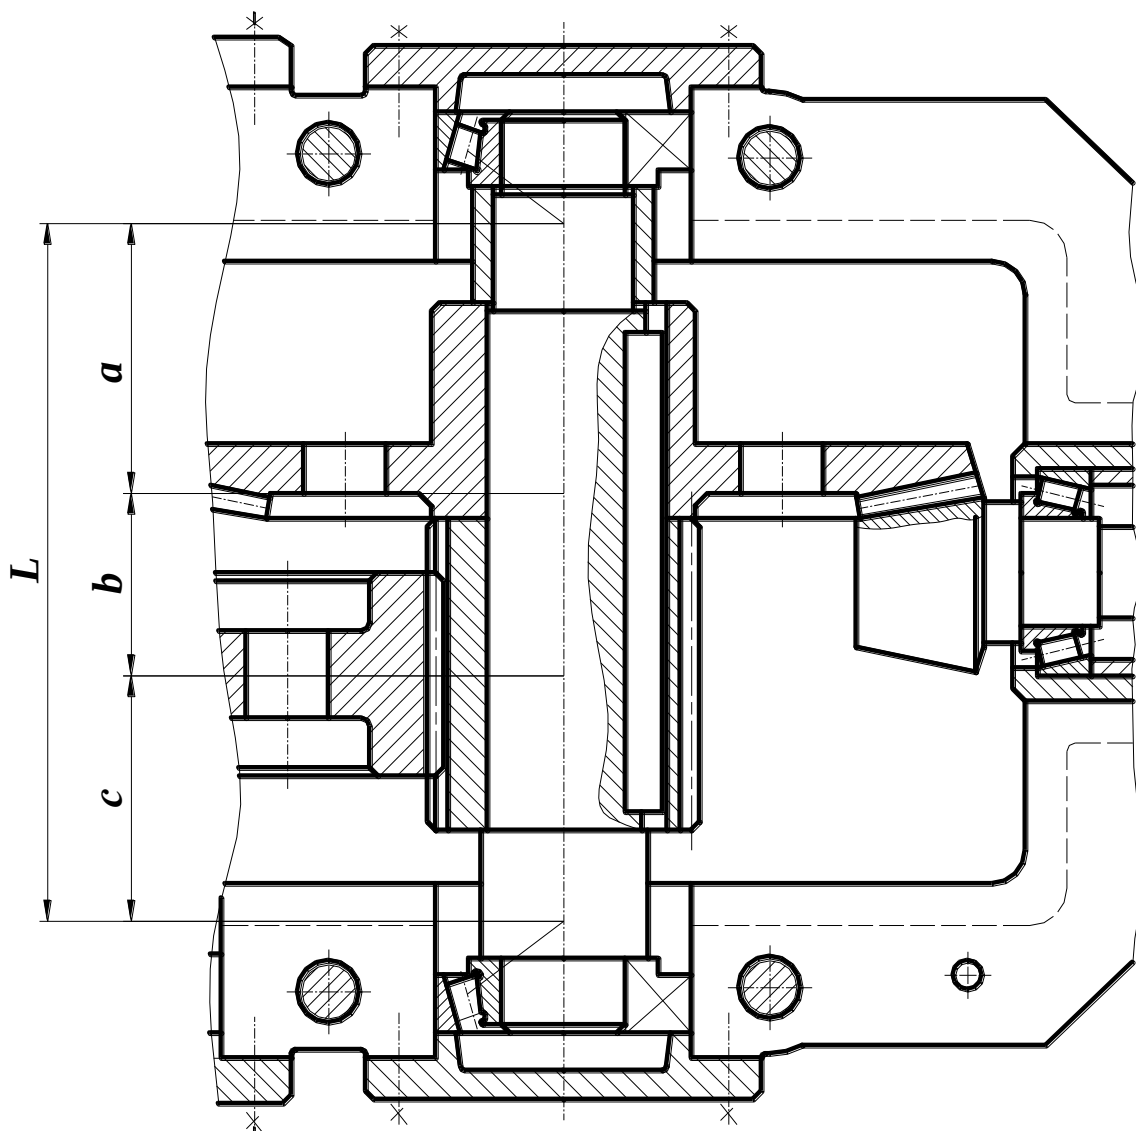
Промежуточный вал коническо-цилиндрического редуктора
